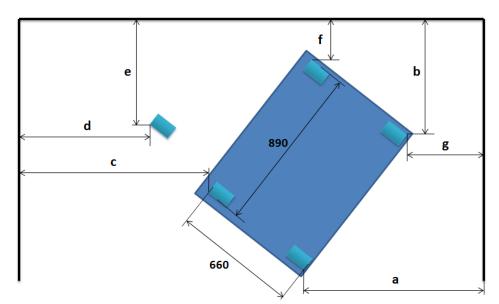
Vista en planta del puesto y la ubicación del polipasto
